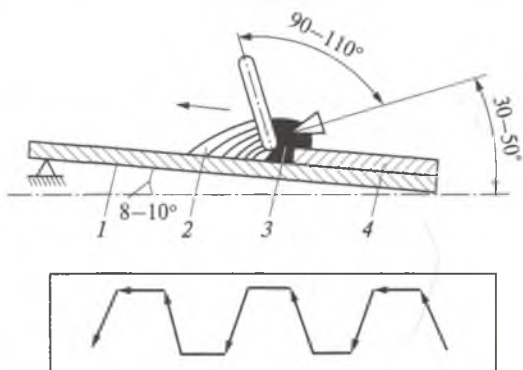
Схема процесса газифлюсовой наплавки латуни:
